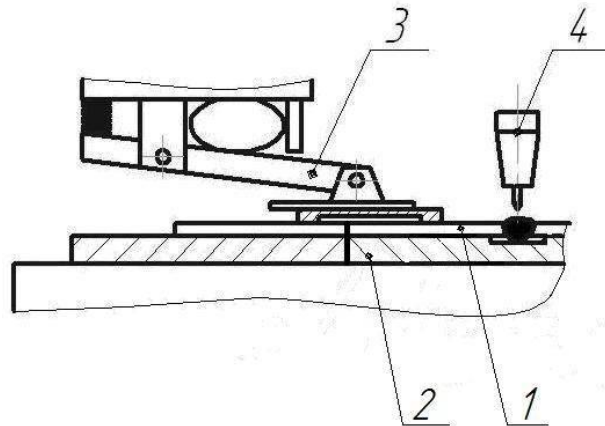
Схема закріплення зразків при зварюванні: 1 – стиковий шов; 2 – мідна підкладка з канавкою; 3 – притискний пристрій; 4 – зварювальна головка
